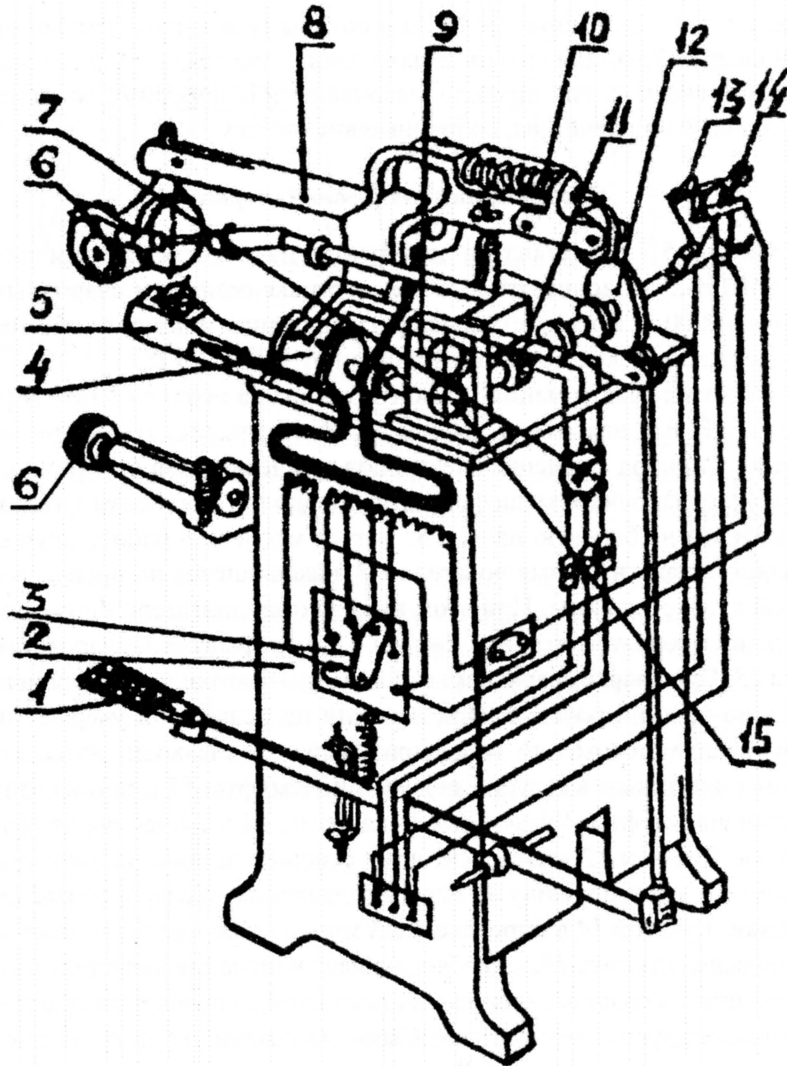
Электрокинематическая схема машины для шовной сварки МШМ-25М:
